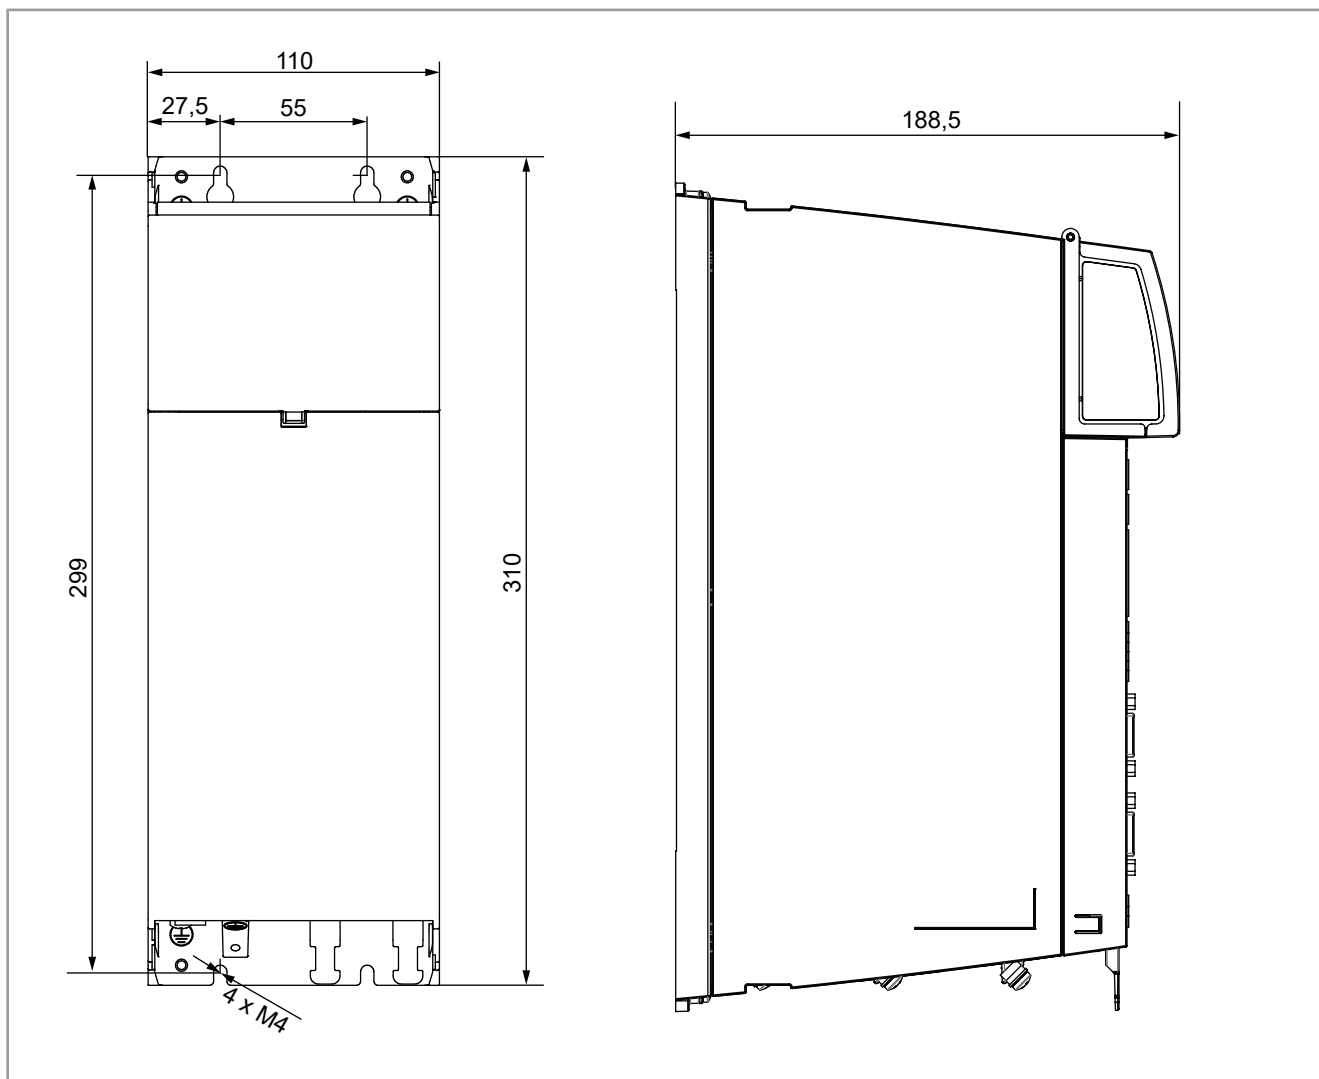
Abmessungen BG2 in mm Cold Plate Montage
